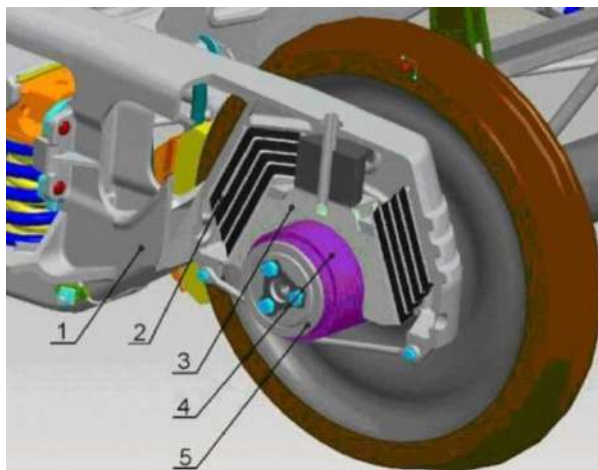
Адаптерный буксовый узел: 1 – боковая рама; 2 – резинометаллические элементы; 3 – адаптер; 4 – подшипник; 5 – колесная пара
